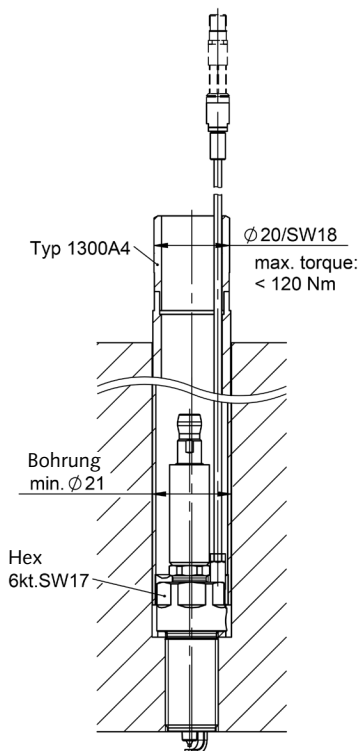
Einbau bei Bohrungsdurchmesser ≥ 21 mm mit Montageschlüssel Typ 1300A4
